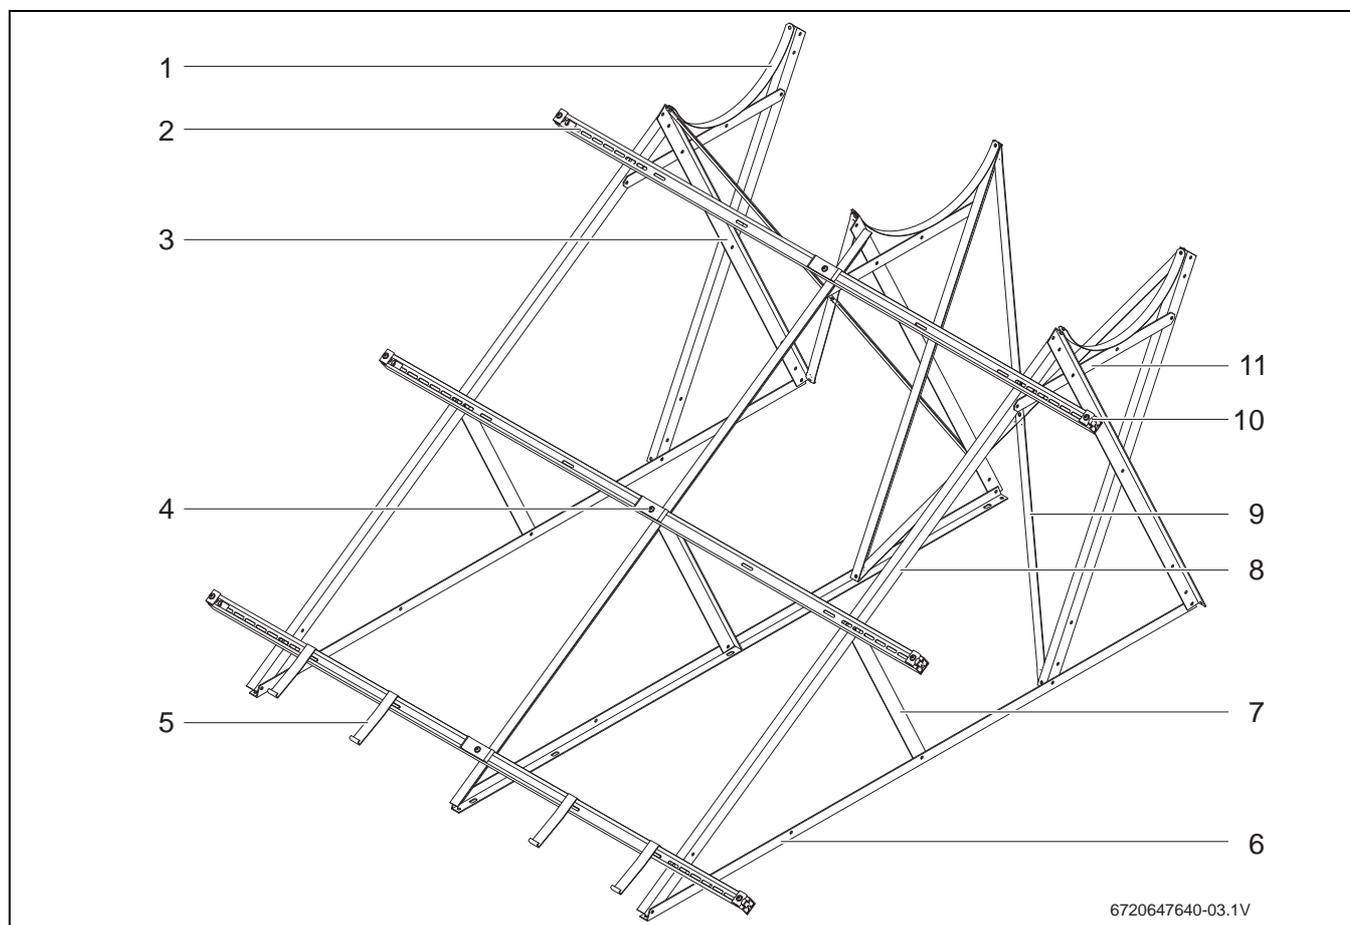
Conjuntos de instalação para 2 colectores: 1 conjunto de instalação de base, 1 um conjunto de instalação de ampliação e um conjunto de instalação adicional
